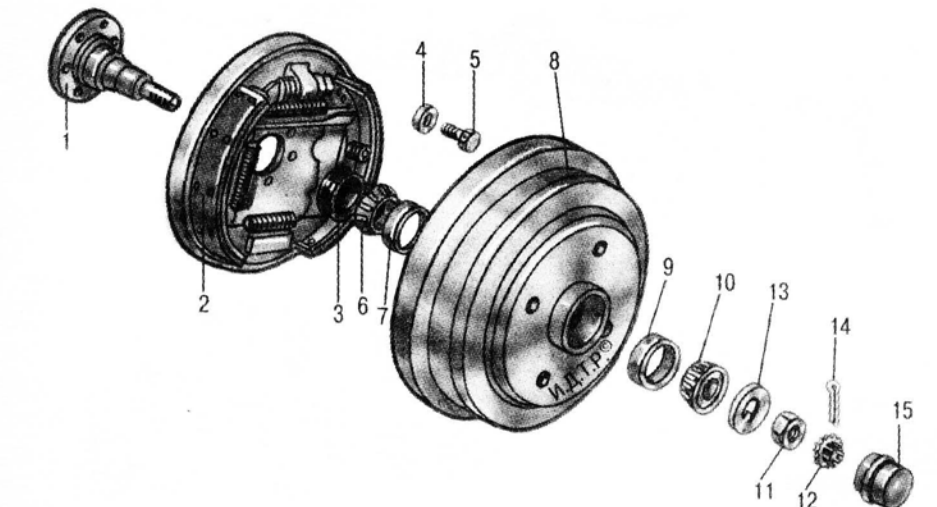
Тормозной барабан (ступица) и его детали: 1 – цапфа; 2 – тормозной механизм; 3 – сальник; 4 – шайба; 5 – болт; 6 – внутреннее кольцо внутреннего подшипника; 7 – наружное кольцо внутреннего подшипника; 8 – барабан (ступица); 9 – наружное кольцо наружного подшипника; 10 – внутреннее кольцо наружного подшипника; 11 – гайка ступицы; 12 – корончатое стопорное кольцо; 13 – упорная шайба; 14 – шплинт; 15 – защитный колпак
